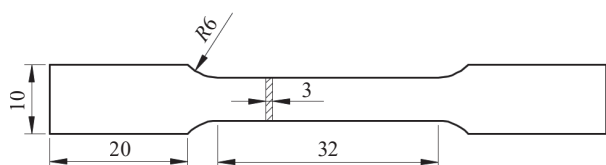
试验钢的拉伸试样尺寸 (单位:mm)
